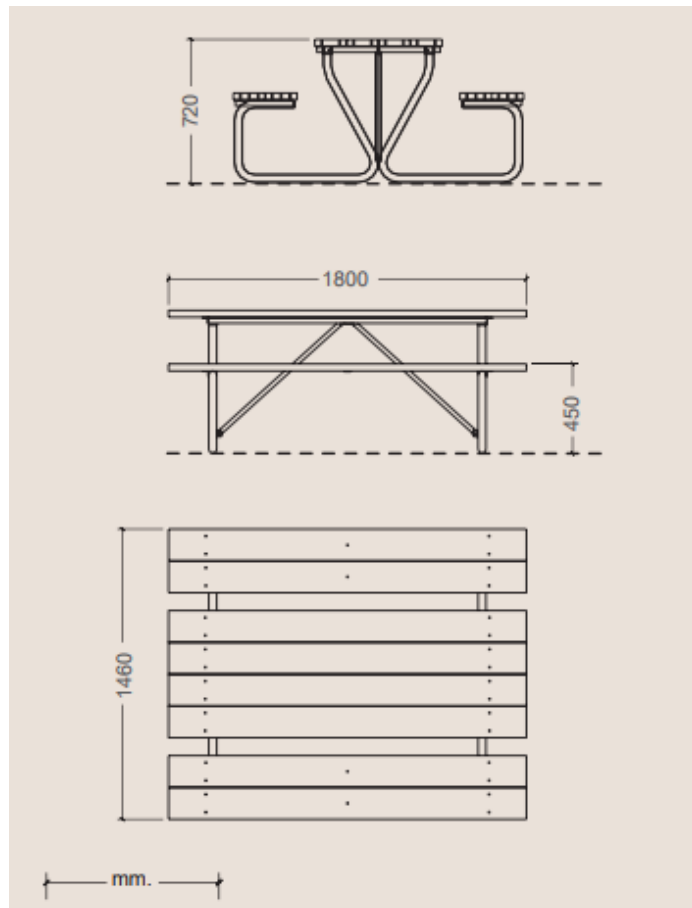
Detalle de perfil, alzado y planta de la mesa picnic. (Fuente: Mobipark).
